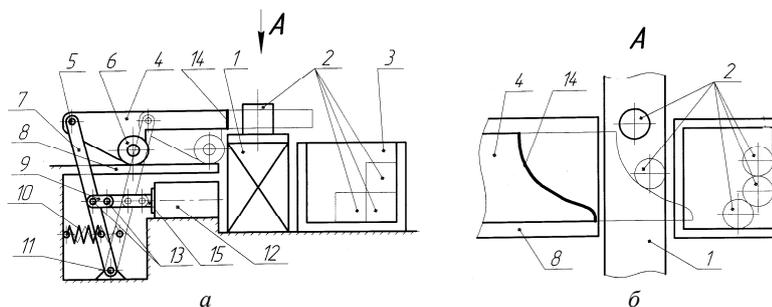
Контрольный механизм: *а* – устройство механизма; *б* – толкатель в рабочем положении; 1 – конвейер, 2 – заготовки, 3 – лоток, 4 – толкатель, 5 – ось, 6 – ролик, 7 – ведущий рычаг, 8 – направляющие, 9 – соединитель, 10 – пружина сжатия, 11 – ось ведущего рычага, 12 – тянущий электромагнит, 13 – ось соединителя, 14 – рабочая поверхность толкателя, 15 – якорь электромагнита
